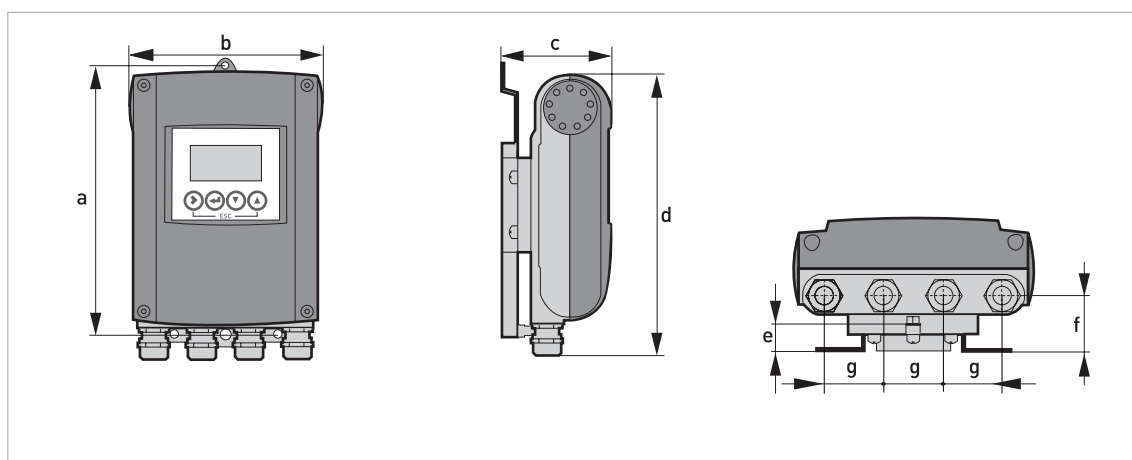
Dimensões da versão para montagem mural, caixa em alumínio
